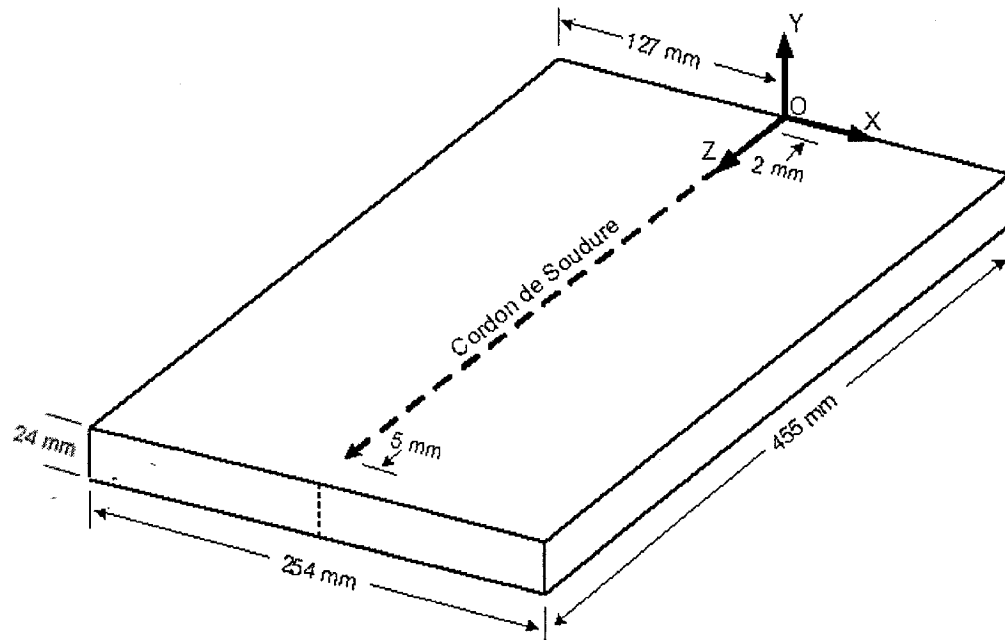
Géométrie du montage utilisé pour la mesure de l'historique thermique d'une passe de soudage
